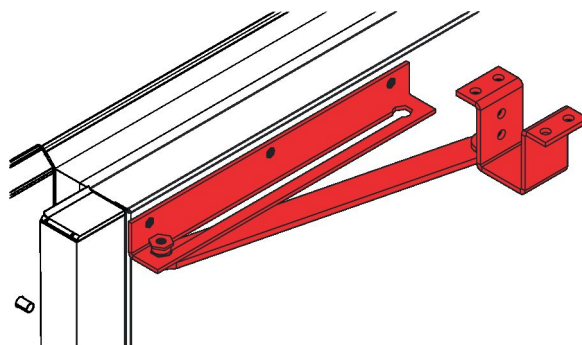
Feststellvorrichtung bei RLT-Geräten für Außenanstellung
